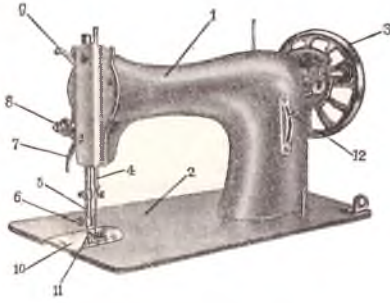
Схема швейной бытовой машины: 1 — рукав; 2 — платформа; 3 — колесо маховое; 4 — игловодитель; 5 — стержень мотора; 6 — винт нажимной лапки; 7 — рычаг подъема стержня; 8 — регулятор натяжения нити; 9 — рычаг нитепротягивателя; 10 — пластина задвижная; 11 — лапка нажимная; 12 — рычаг направления подачи
